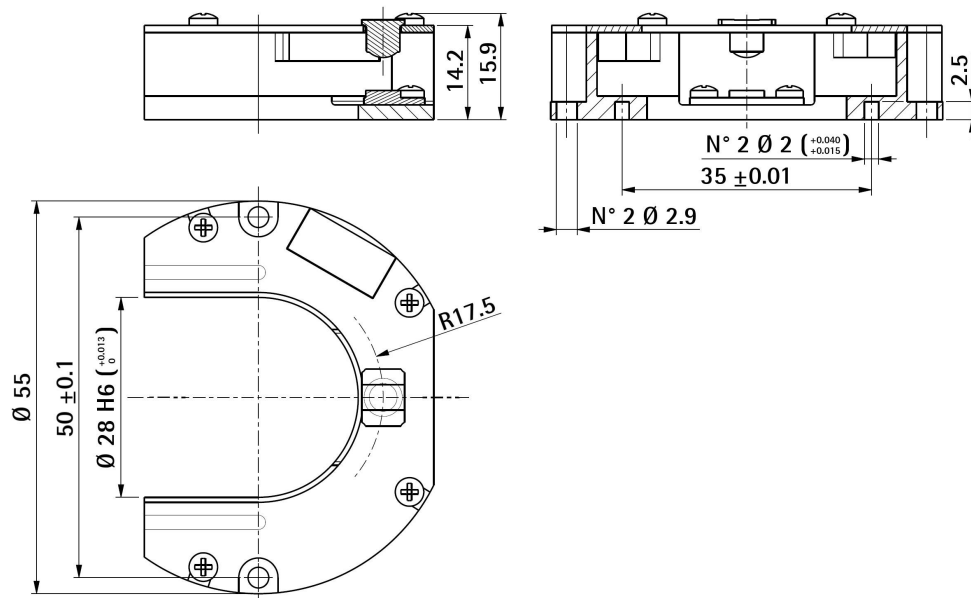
Dimensioni di ingombro dell'encoder AMM5B
